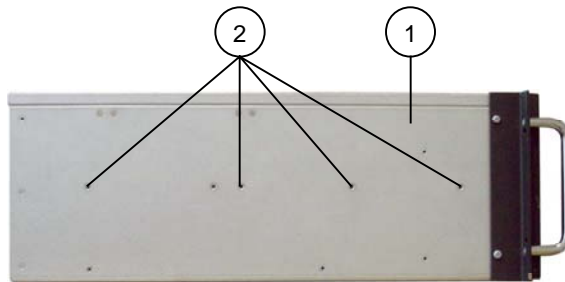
Gewindebohrungen (M4) für Befestigung einer Teleskopschiene
